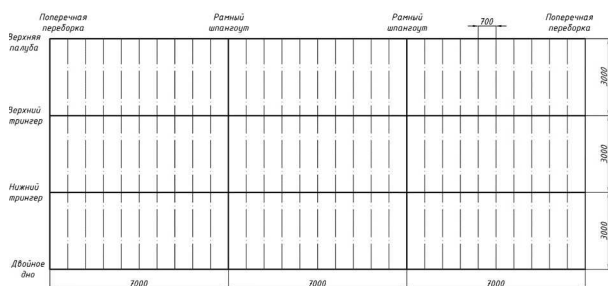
Расчетная схема набора базового бортового перекрытия, набранного по поперечной системе набора
